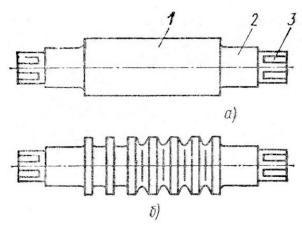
Прокатные валки: а - гладкий; б - калиброванный
